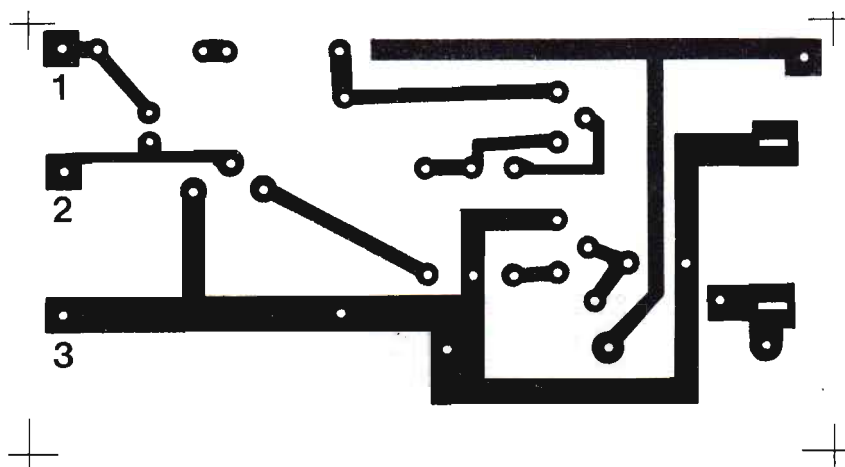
Disegno in dimensioni reali del circuito stampato sul quale va realizzato il modulo ricevitore.
